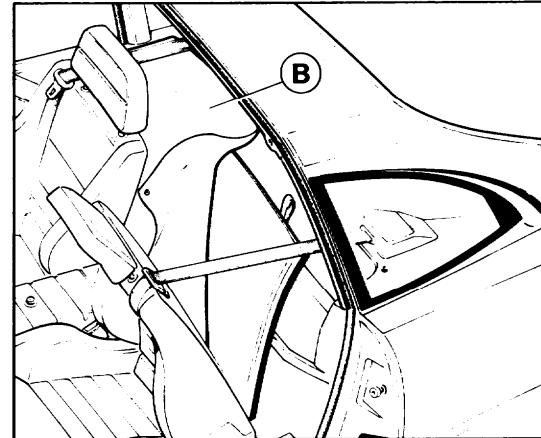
26 - 27 - Capot (démontage et montage)
